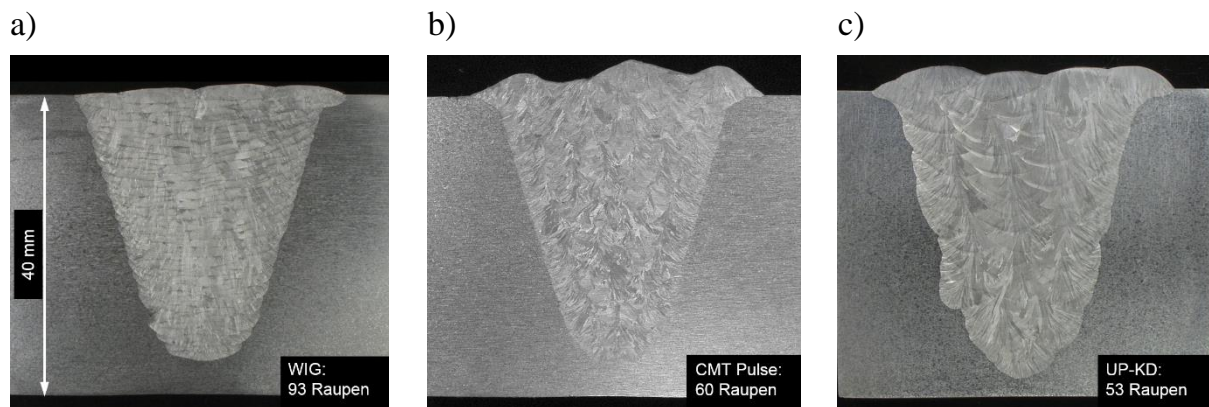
Makro-Querschliffe der Füllschweißungen: a) WIG-KD, b) CMT Pulse, c) UP-KD
